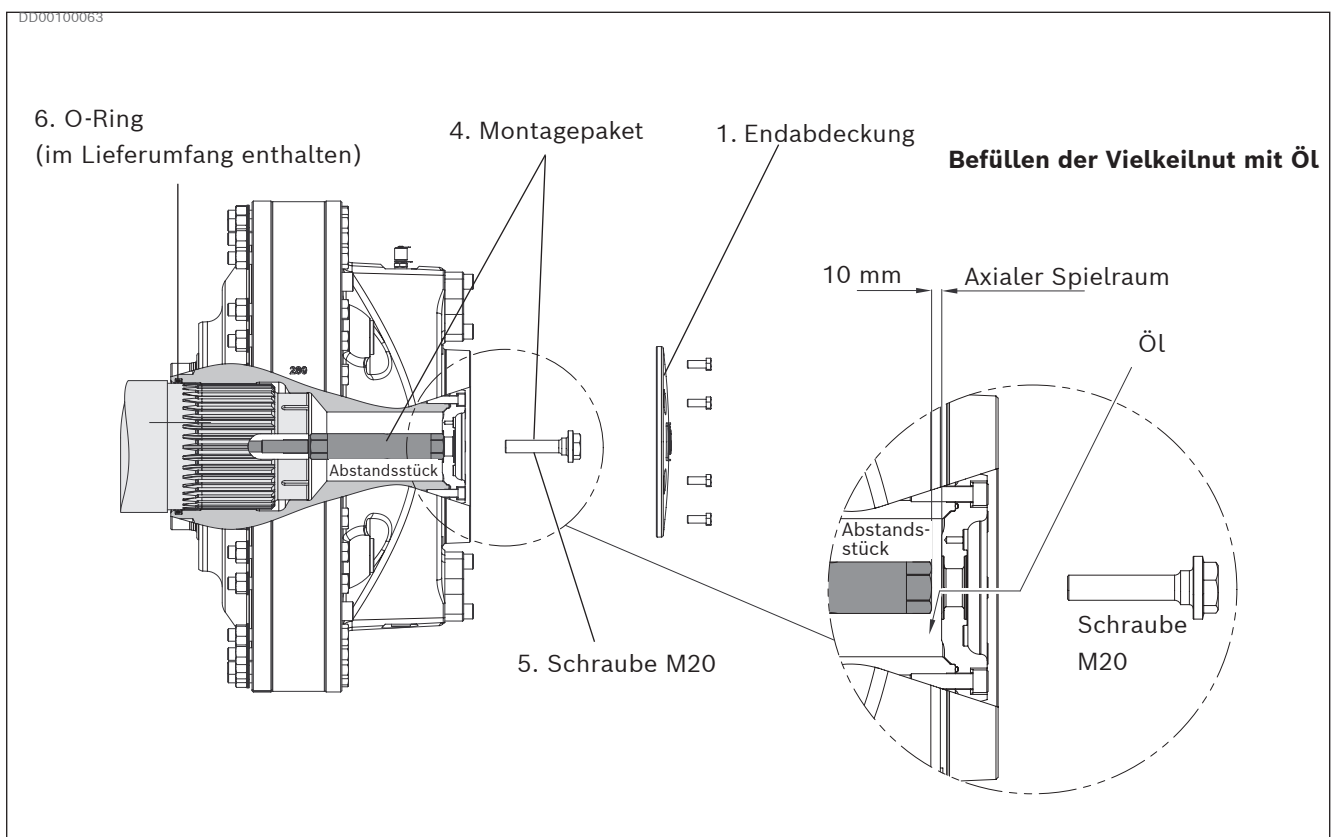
Befestigen Sie den Motor mit Vielkeilnut mithilfe des Montagepaketes, waagerechte Montage.
